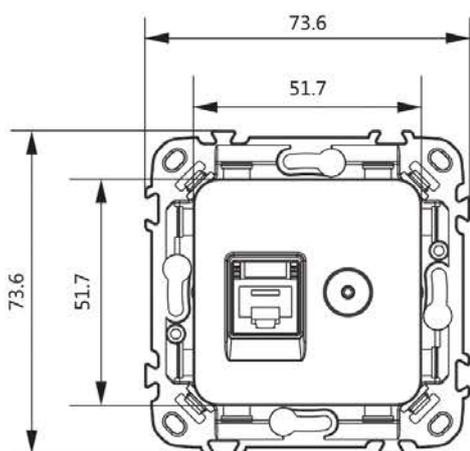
Габаритные и установочные размеры розеток (лист 1 из 4) / Figure 2 – Overall and installation dimensions of sockets (sheet 1 of 4) / 2-сурет – Розеткалардың жалпы және орнату өлшемдері (4-ден 1-парақ)
